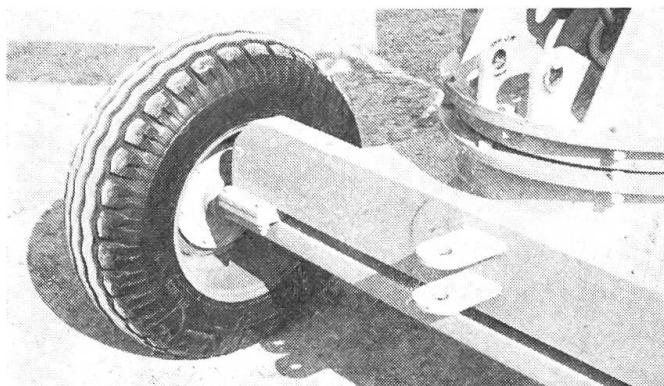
Achse – mit 8 Schrauben befestigt – kann gut gegen Achse mit Bremsen ausgetauscht werden.
